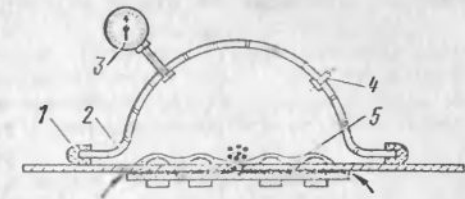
Приспособление для местной проверки герметичности в заклепочном соединении
